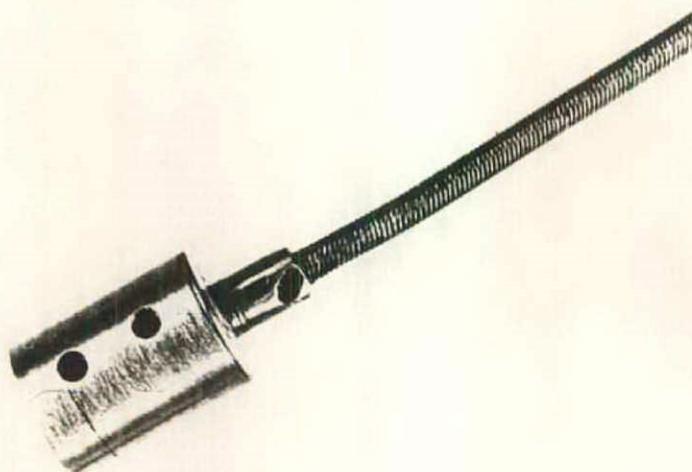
Flange de conexão veio flexível/eixo do motor.
